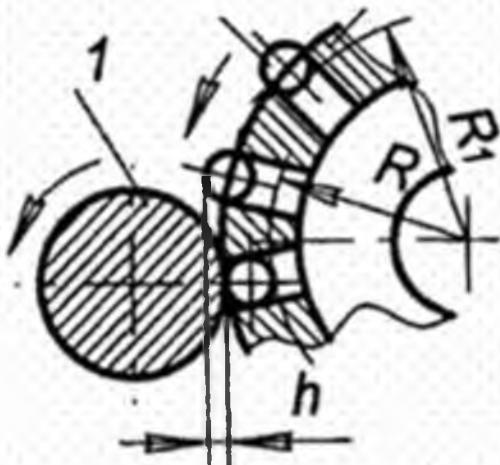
Схема відцентрової обробки поверхні кульками
